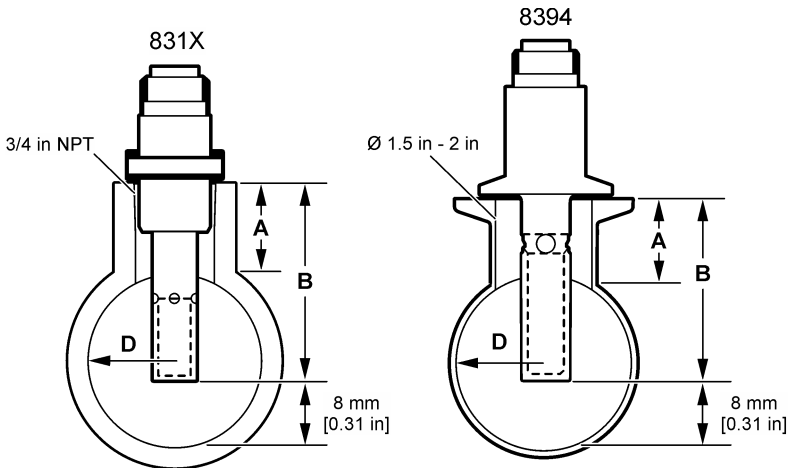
(#) toont de sensoren die in een leiding zijn geïnstalleerd. [Afbeelding 2](#) en [Tabel 3](#) geven de diepte en leidingdiameter van de sensorinstallatie.
